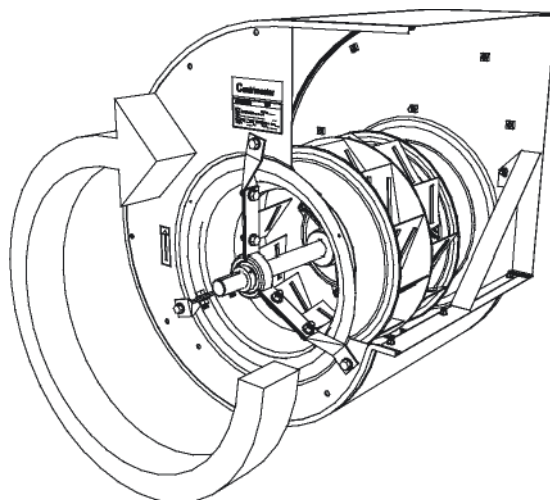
Sentido correcto de rotación de una turbina LB y HB.
